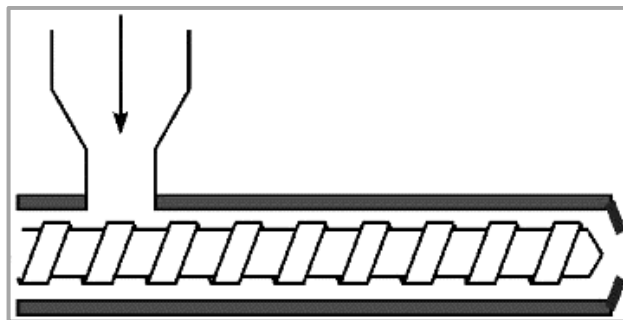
Sistema de compresión y extrusión por tornillo sin fin [35].
